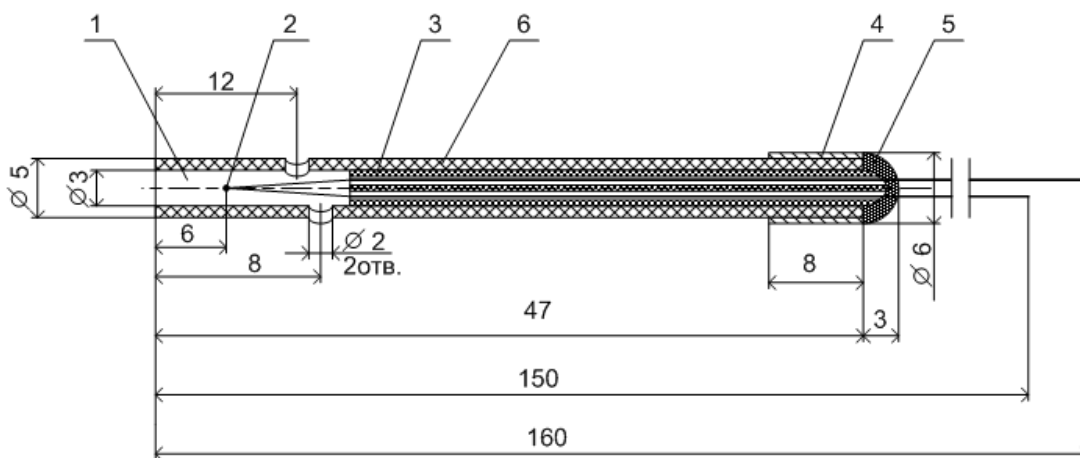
Загальний вигляд термоперетворювача типу ТІР-0182: 1 – камера гальмування; 2 – з'юст термопар; 3 – електроізоляційна трубка; 4 – металева втулка; 5 – термоцемент Ф50; 6 – захисний корпус.
